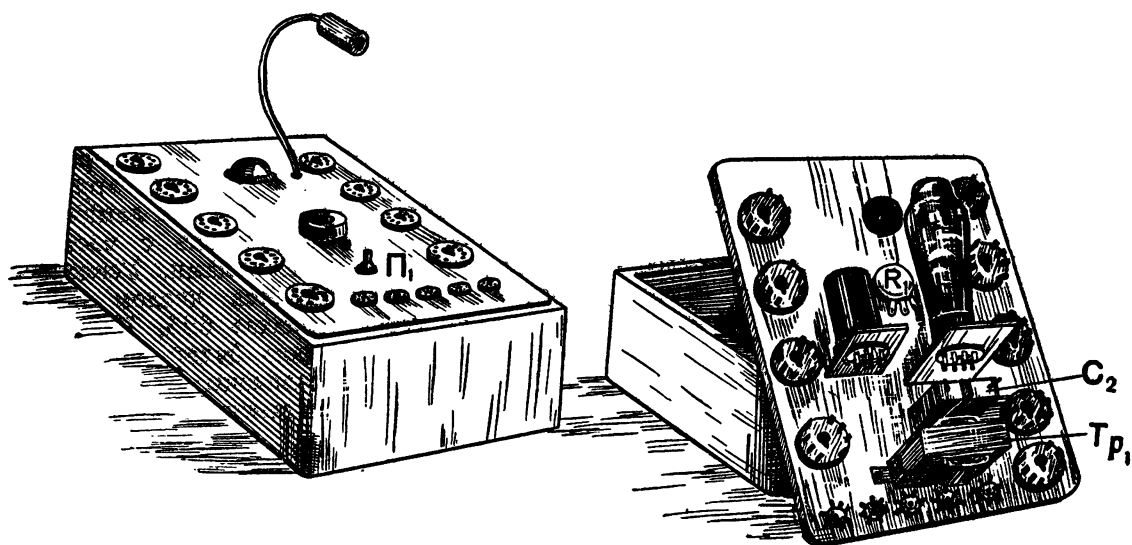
Размещение деталей испытателя ламп и общий вид прибора.
